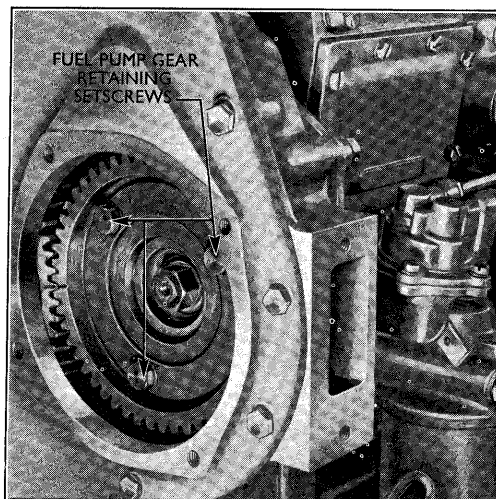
Skruerne der holder pumpedrevet til pumpens flange.
